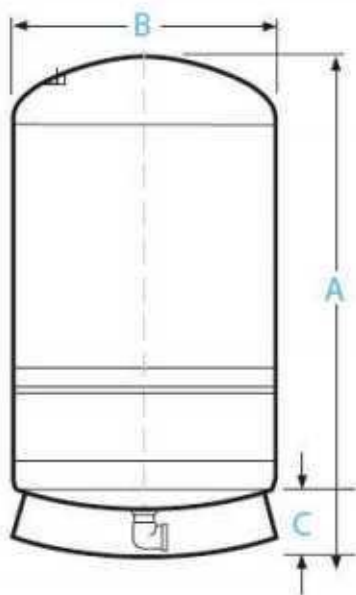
Rozměry čerpadla E-DEEP [64]
